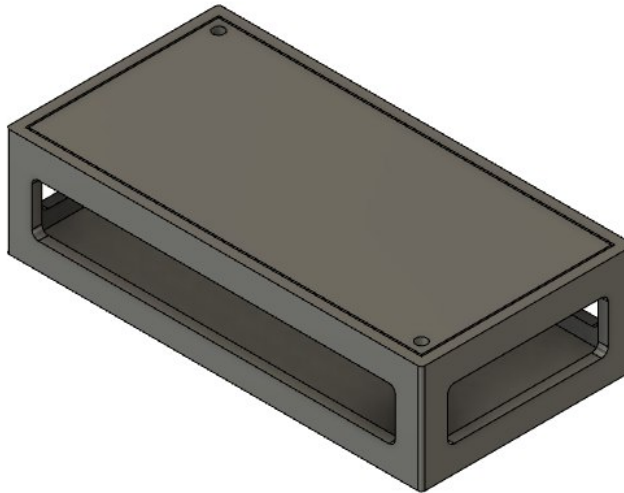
Projeto de caixa de proteção do módulo de controle
